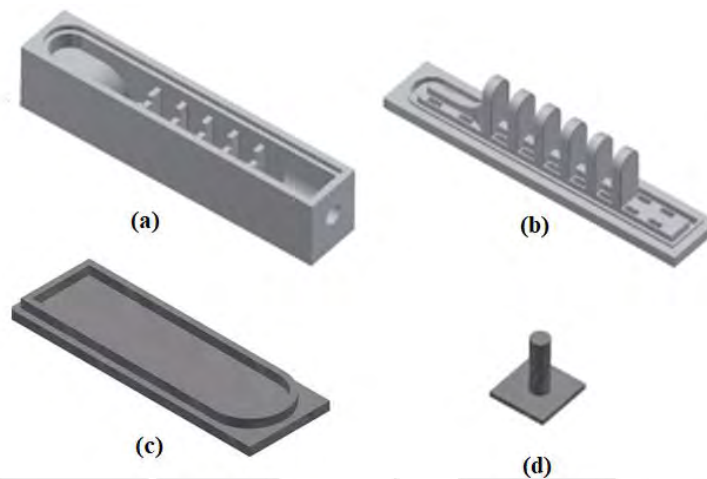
Molde diseñado para actuador blando: (a) Parte Inferior, (b) Parte Superior, (c) Parte Base, (d). Parte del Conducto
